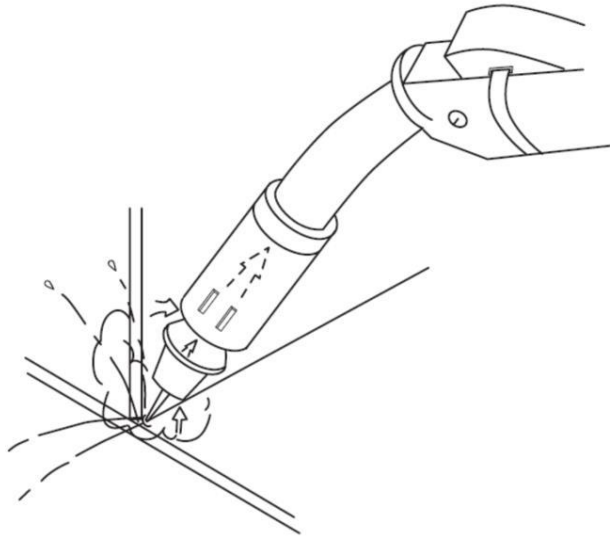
Pistola de soldadura con extractor integrado.
